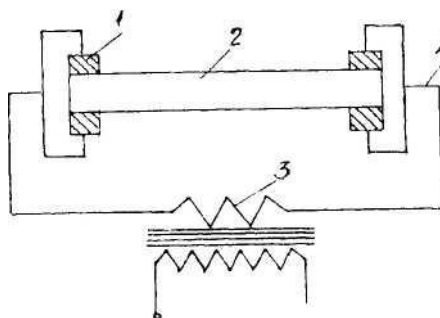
Схема установки электроконтактного нагрева [1]: 1 - контакты; 2 - заготовка; 3 - трансформатор; 4 - подводящие провода
